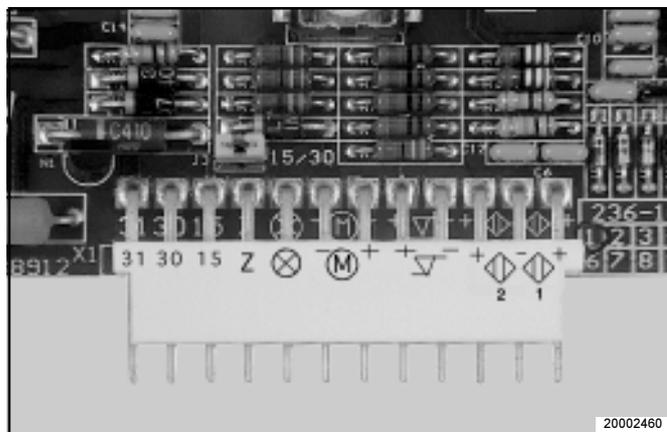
Bornes de raccordement de la plaque de circuits imprimés
